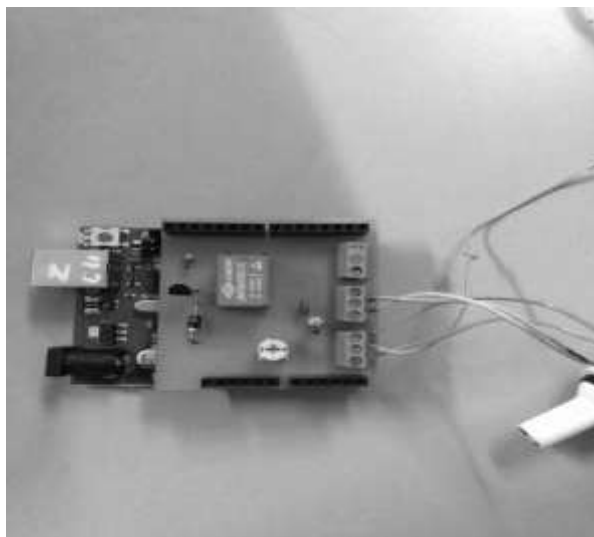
Ensamble de los componentes electrónicos en las PCB.
